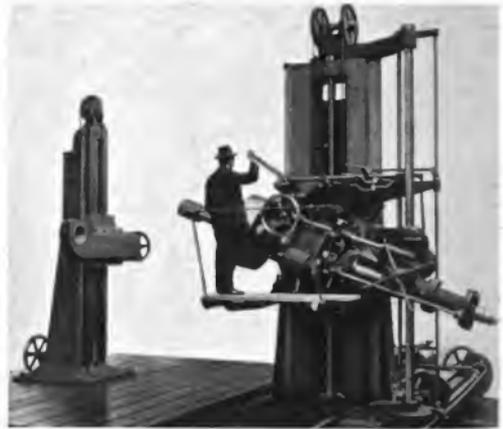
Horizontal-Bohr- und Fräsmaschine mit schwenkbarem Spindelkasten
